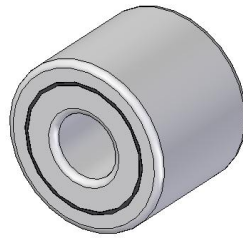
Modelado del rodamiento alojado en el anclaje de la columna de dirección
